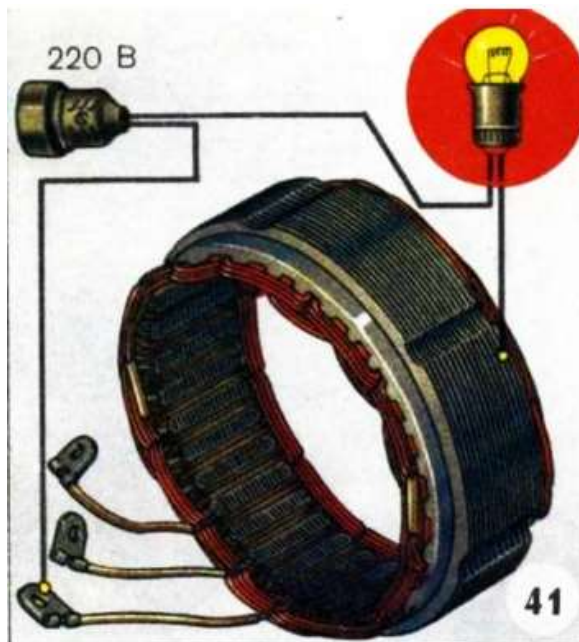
Проверка обмотки статора на замыкание с корпусом
